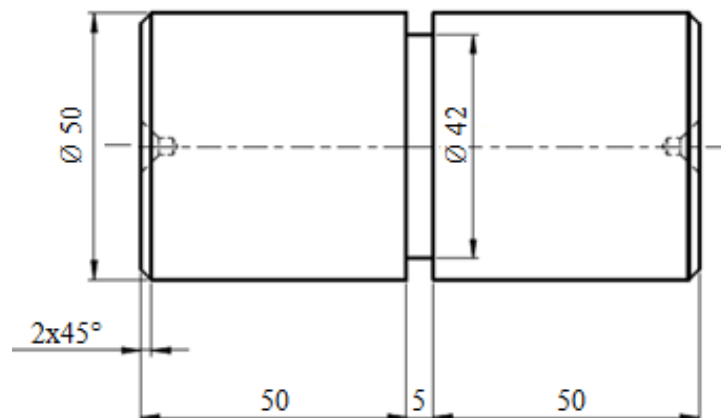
Dimensões dos corpos de prova ensaiados
